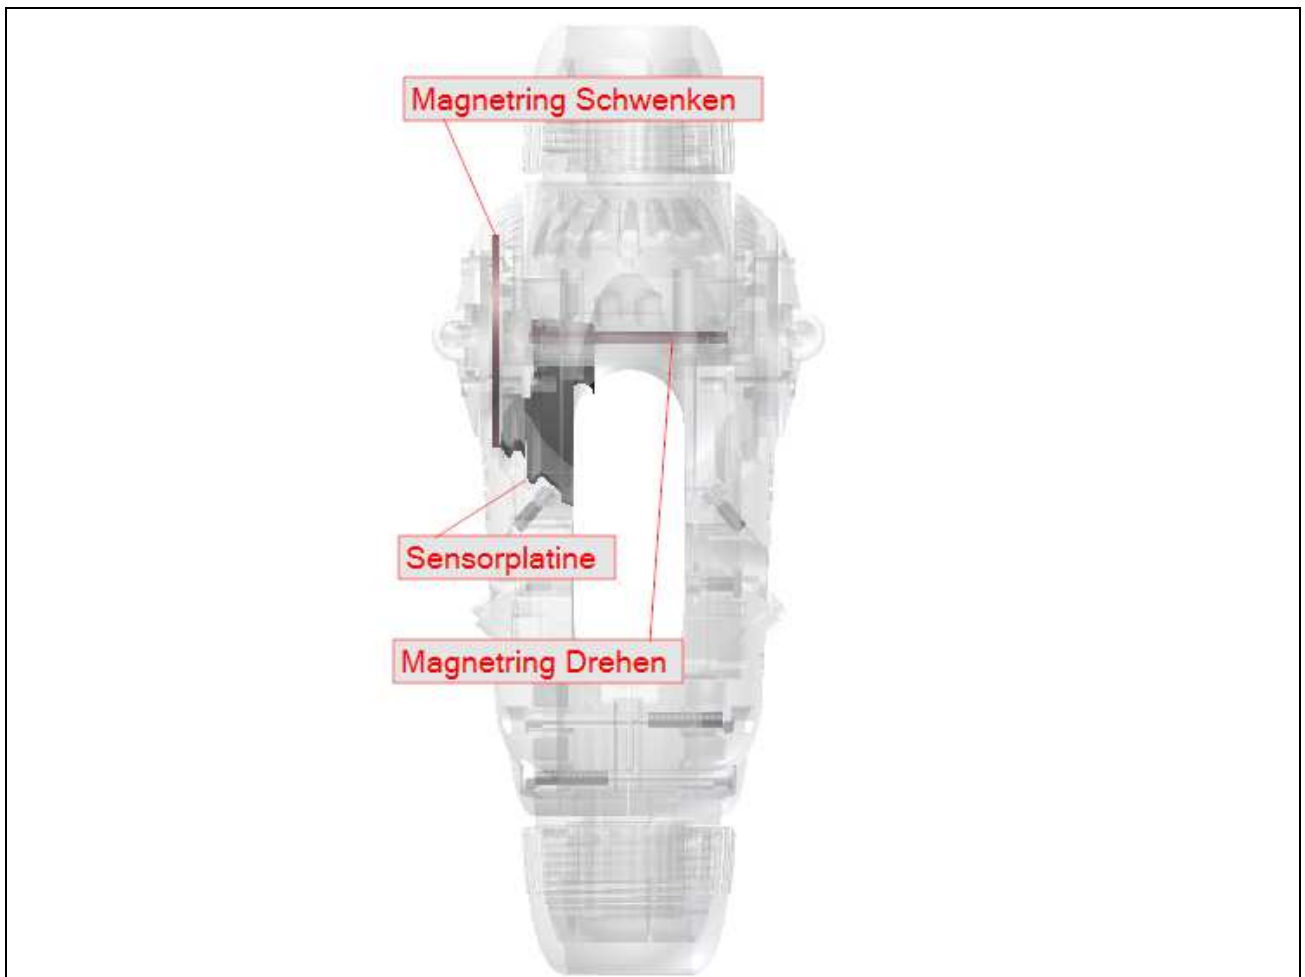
Einbausituation des Sensors im Gelenk RL-50-001 /-002 /-003
